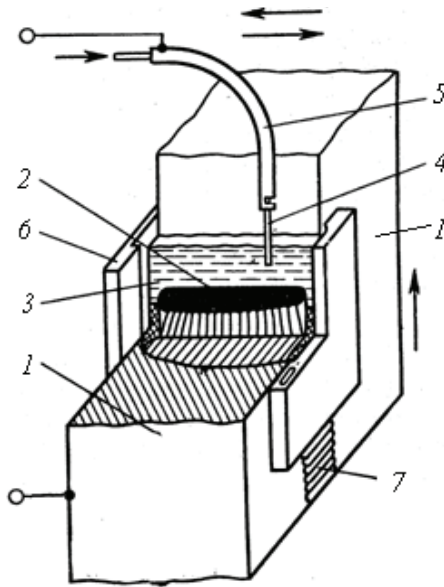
Схема электрошлаковой сварки: 1 — свариваемые заготовки; 2 — сварочная ванна расплавленного металла; 3 — шлаковая ванна; 4 — сварочная проволока; 5 — мундштук; 6 — ползуны (формирующие устройства); 7 — затвердевший сварной шов
